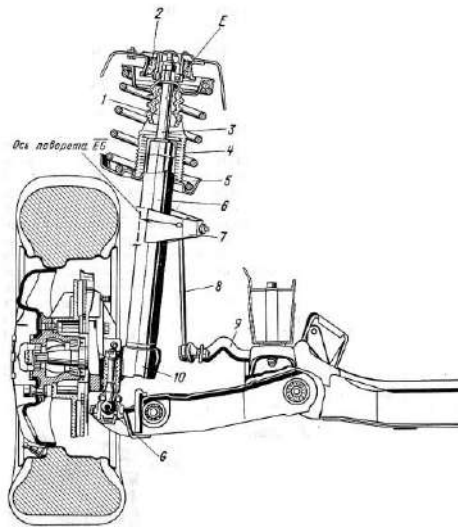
Передня підвіска з пружинними стійками і маятникових стабілізатором автомобіля «Опель-сенатор»: 1 - пружний елемент; 2 - масивна гумова деталь; 3 - шток; 4 - захисний чохол; 5 - опорна чашка; 6 - резервуар; 7 - кронштейн; 8 - шарнір стійки; 9 - плече стабілізатора; 10 - опора підшипника колеса
